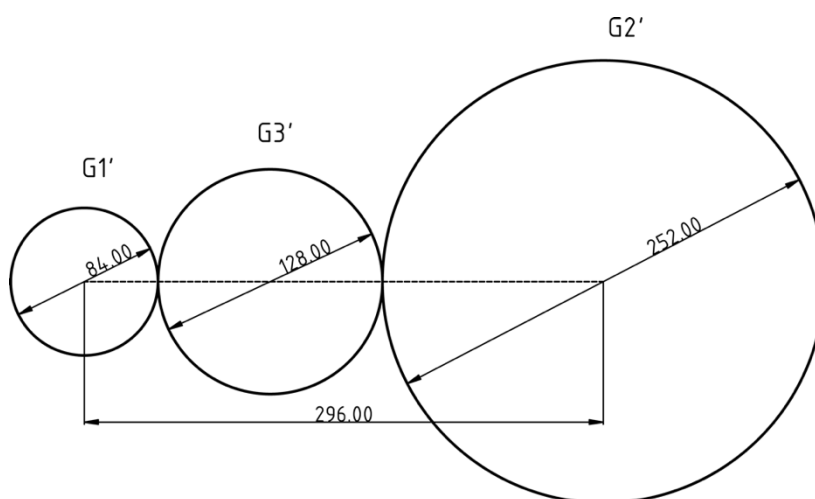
Dimensiones del tren de engranajes para la Opción N° 1.
